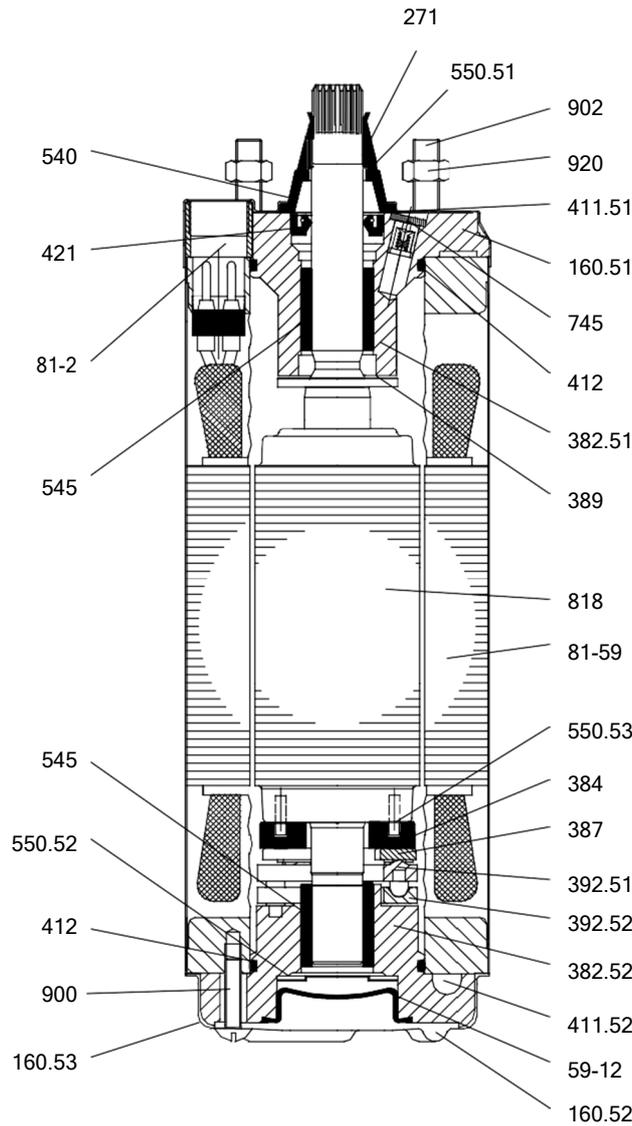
Desenho em corte do tipo de bomba UPachrom CN
